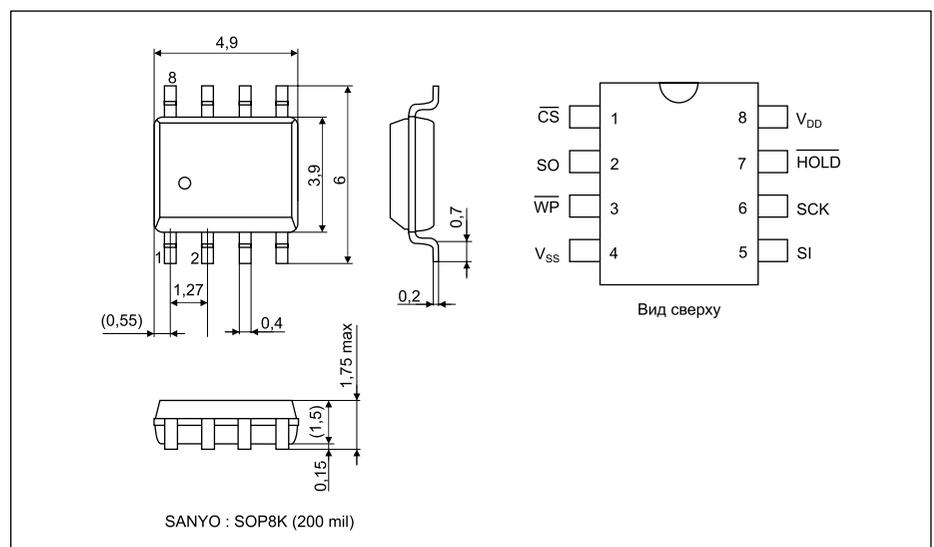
Назначение выводов и габаритные размеры LE25S40MB/LE25U20AMB в корпусе SOP8K
